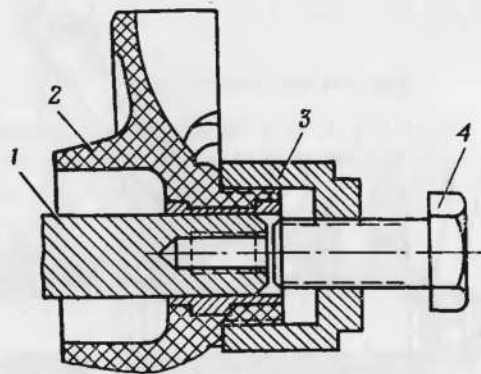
Установка съемника для спрессовки крыльчатки водяного насоса:
